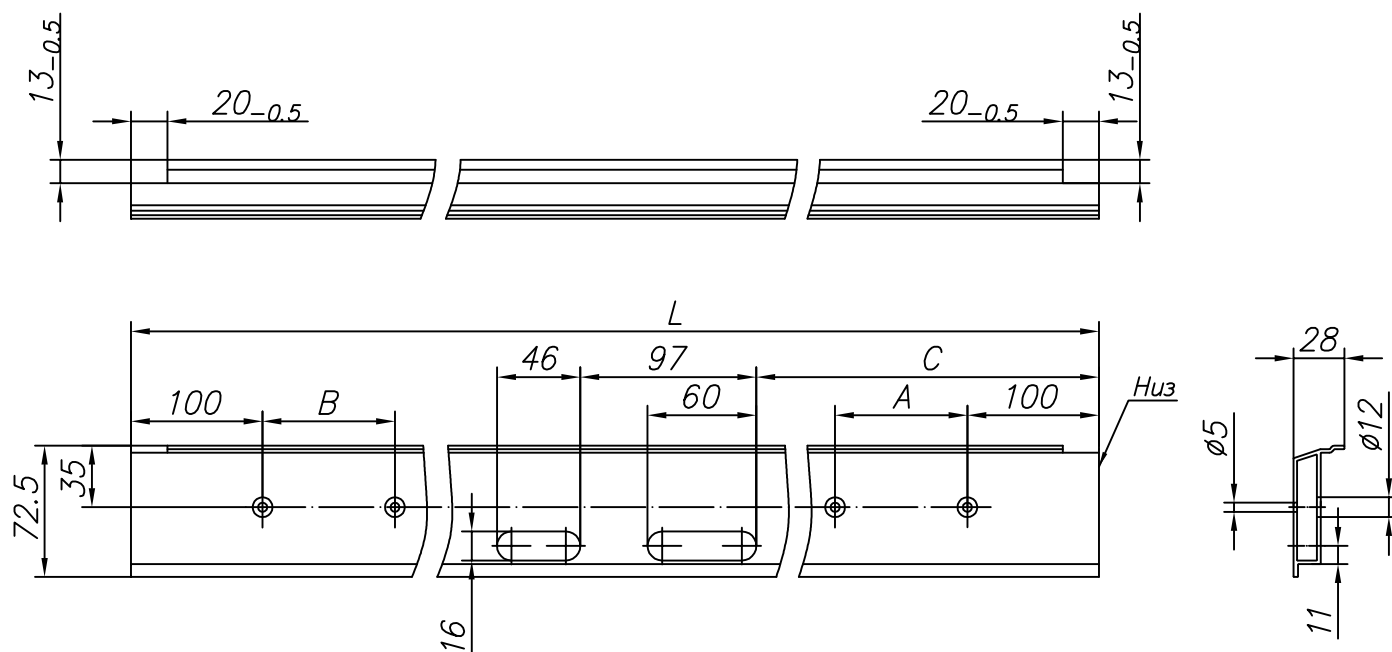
Изготовление притвора с пазом для ответной пластины замка из профиля FLGU.400.0505 (открывание внутрь, вправо)
